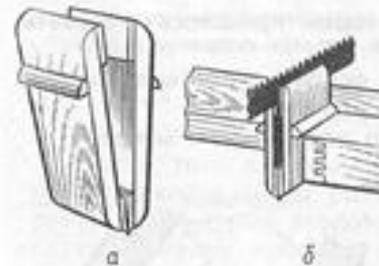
Тиски для заточки пил (а); установка тисков и полотна (б).
